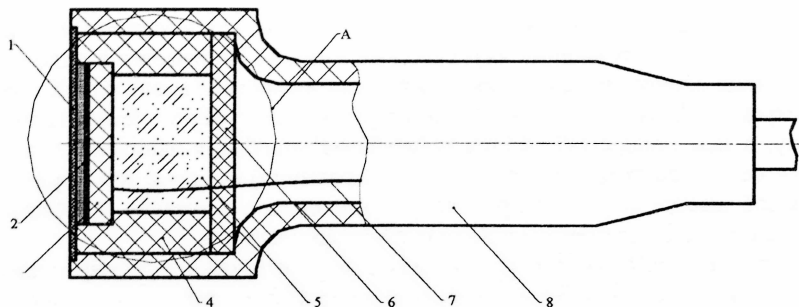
Зонд новой конструкции: 1- второй согласующий слой; 2- первый согласующий слой; 3- пьезокерамическая пластина; 4- втулка акустической развязки; 5- демпфер; 6- катушка индуктивности; 7- провод коммутации; 8- корпус.
